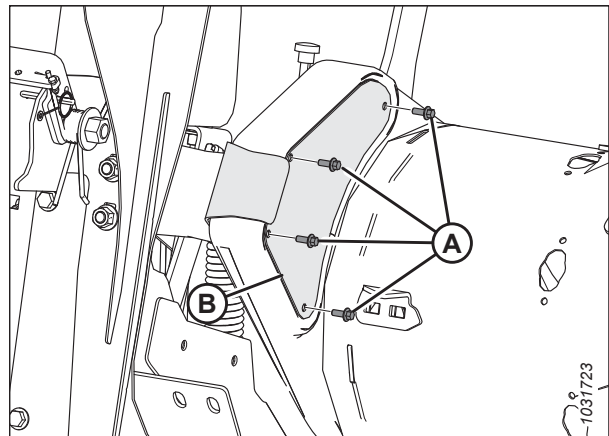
Linke Seite des Einzugschnecken-Getriebes – Rückansicht
